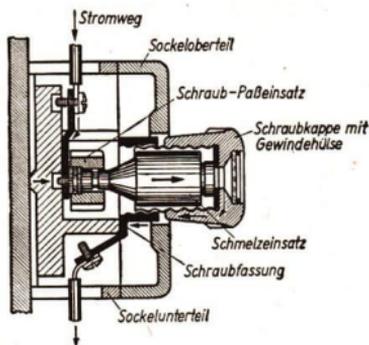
/2. Stromweg in einer Schmelzsicherung: Kontaktplatte — Schmelzeinsatz — Gewinde des Deckels — Gewinde des Gehäuses
